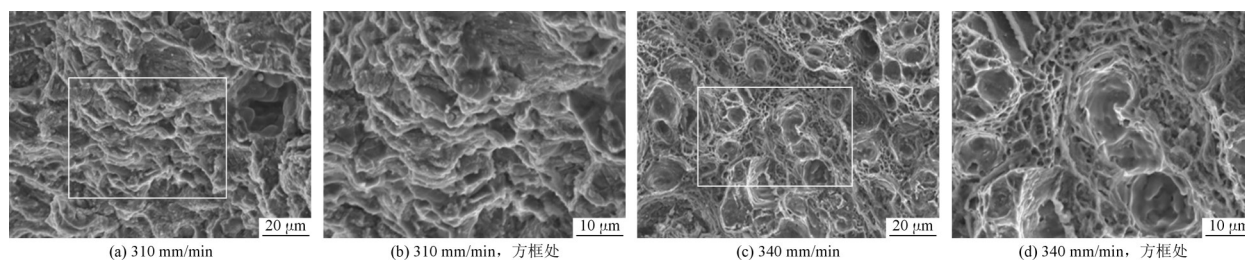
不同焊接速率下试样的拉伸断口形貌
